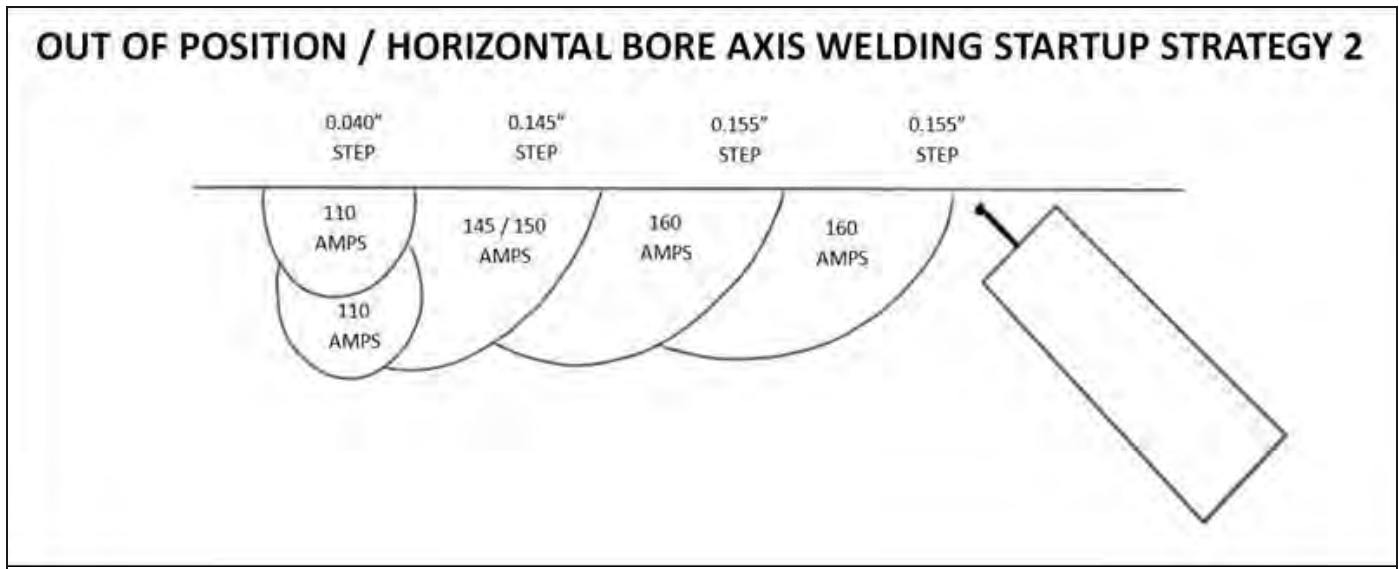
ESTRATEGIA 2 PARA INICIO DE SOLDADURA EN EJE DE ORIFICIO FUERA DE POSICIÓN/HORIZONTAL
